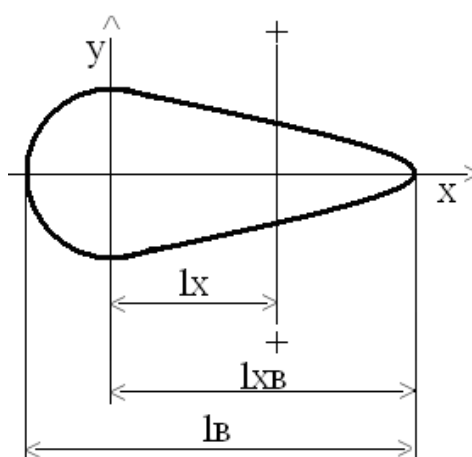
Схема сварочной ванны:  $l_в$ - длина сварочной ванны;  $l_{xв}$ - длина хвостовой части сварочной ванны; + - перекрещивающиеся риски;  $l_x$ - промежуточное положение перекрещивающихся рисок
